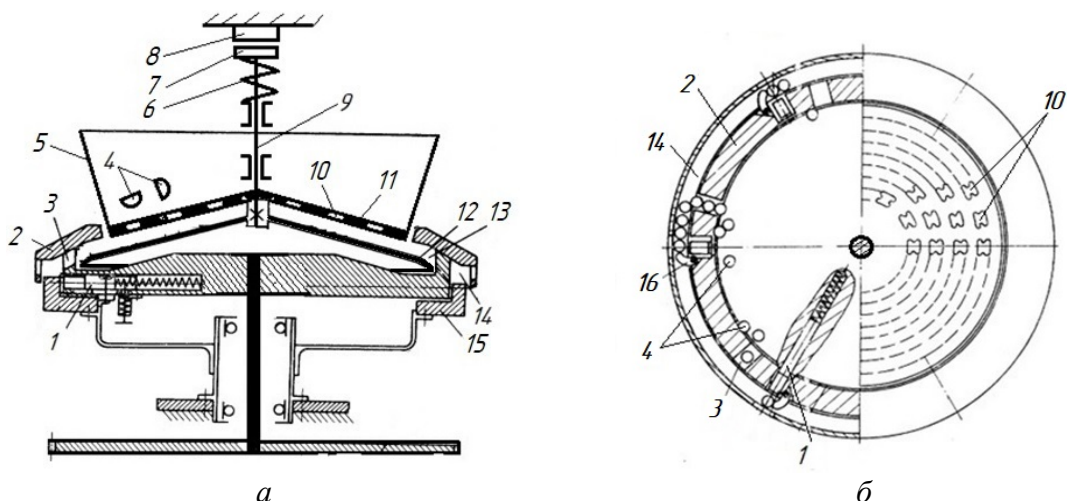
Схема роторного автомата питания планетарного типа для автоматической загрузки деталей типа низких колпачков:
